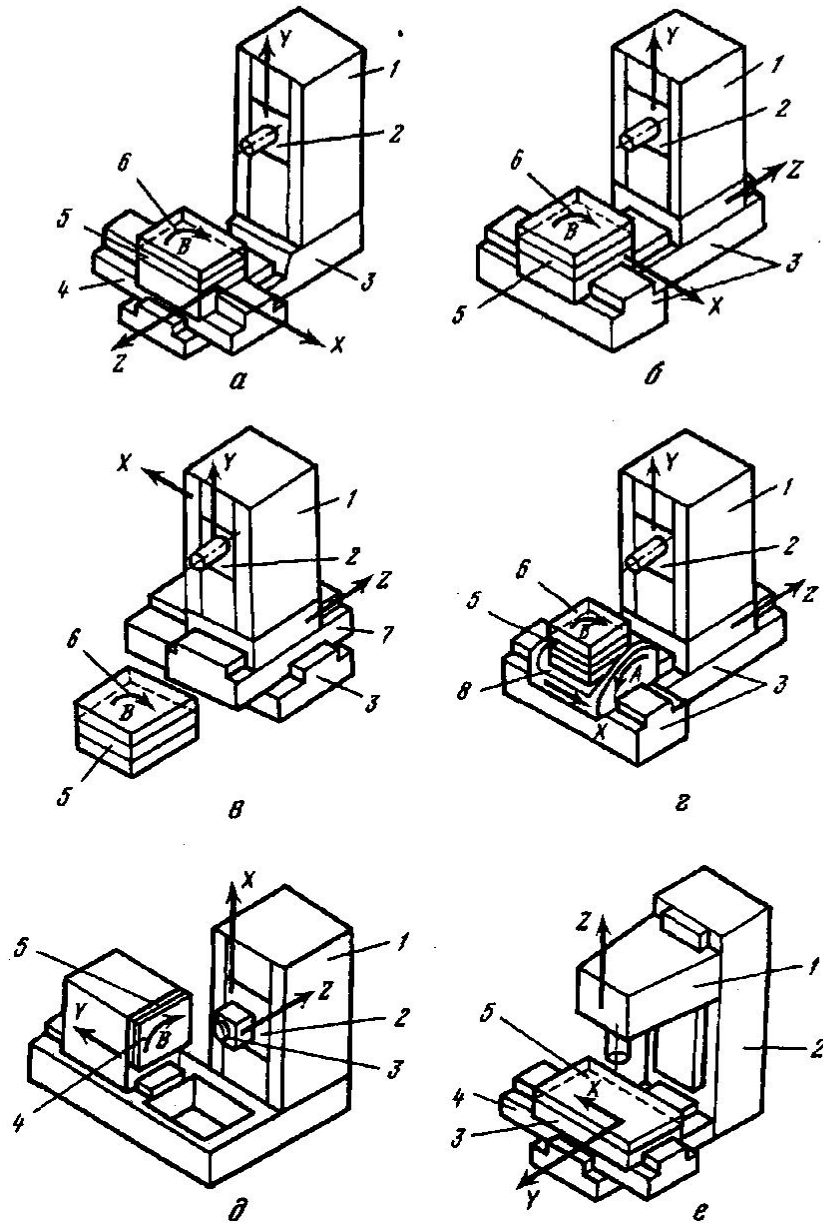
Основні компоновки верстатів у ГВМ для обробки корпусних і плоских деталей
